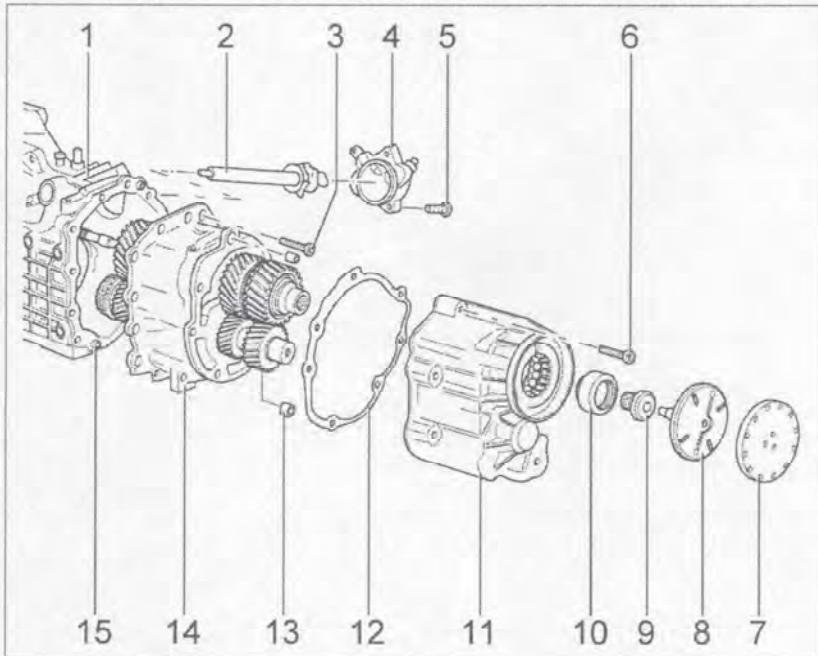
Корпус подшипников и крышка коробки передач:
